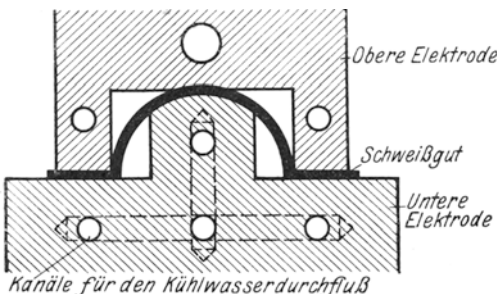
Elektroden einer Formeisen-schweißmaschine.
